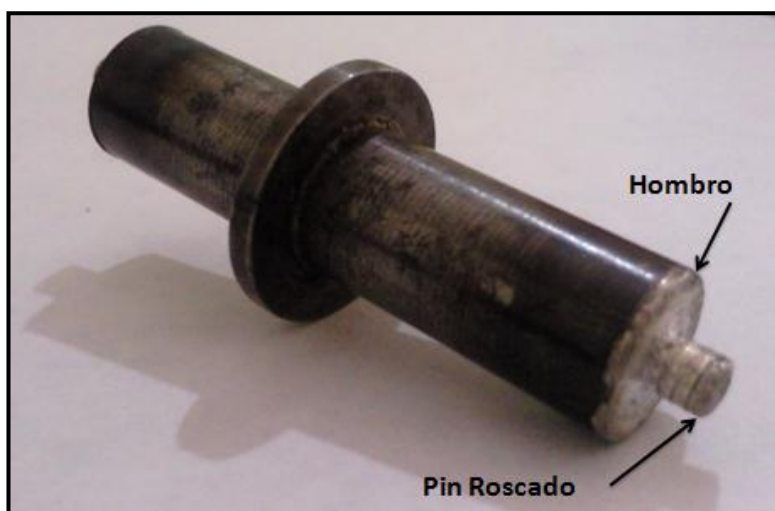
Herramienta fabricada para la realización de las soldaduras
